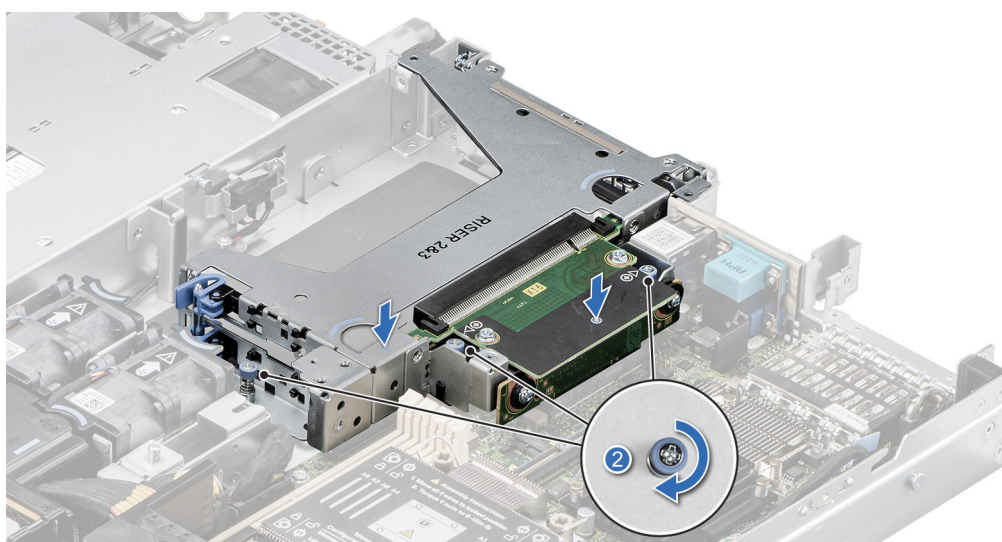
Instalación de las tarjetas elevadoras 2 y 3
